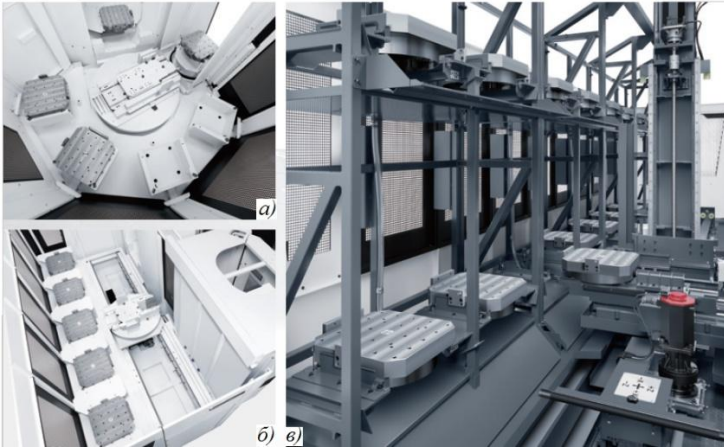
Варіанти ГВС на базі верстатів DMG NHX 5000
